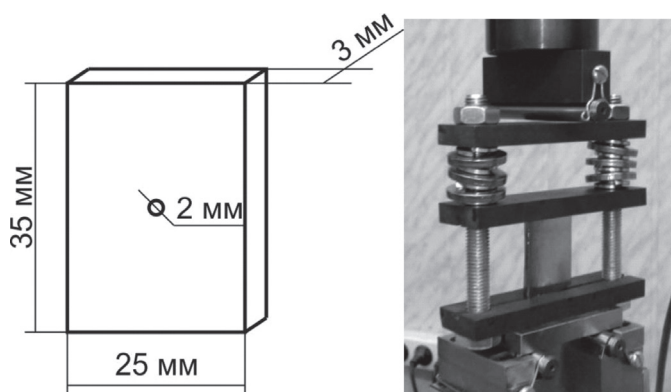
Схема образца и внешний вид приспособления для создания сжимающих напряжений
